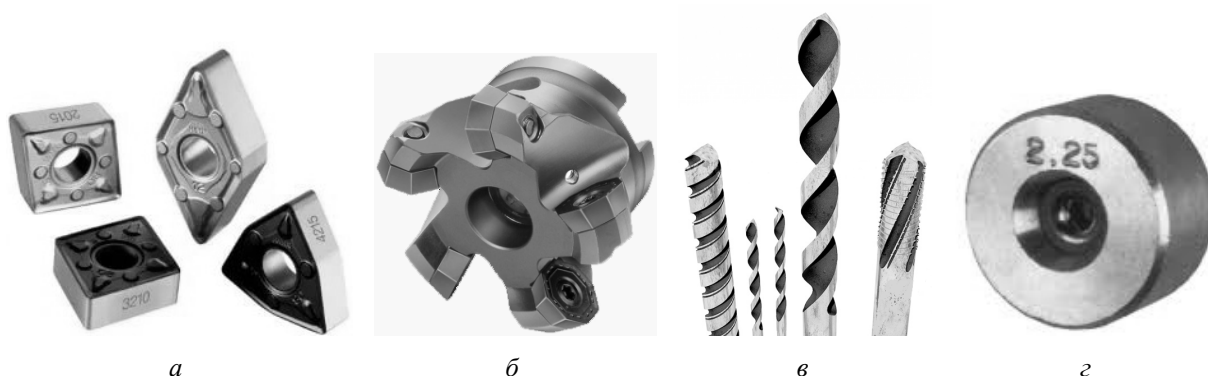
Вироби з металокерамічних твердих сплавів: *а* – пластинки до ріжучого інструменту; *б* – бурова коронка з металокерамічними вставками; *в* – цільні інструменти; *г* – філь'єра
